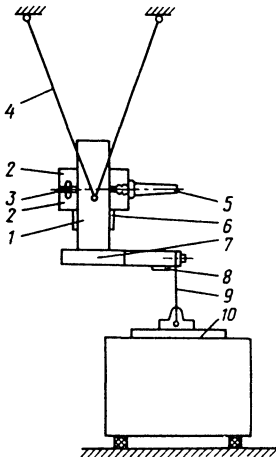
Схема зажима для крепления рабочих лопаток при усталостных испытаниях
